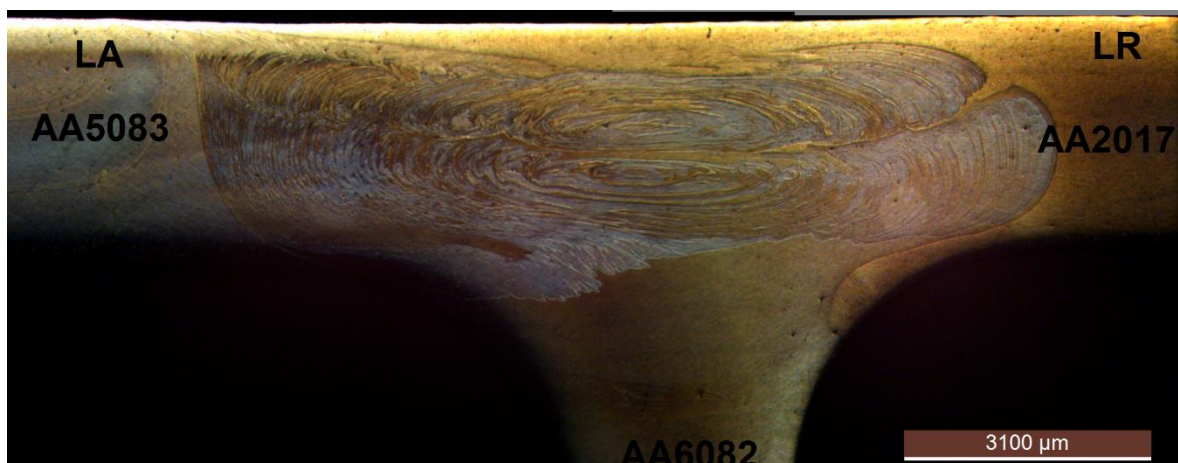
Macrografia da soldadura 562BRP-2.
